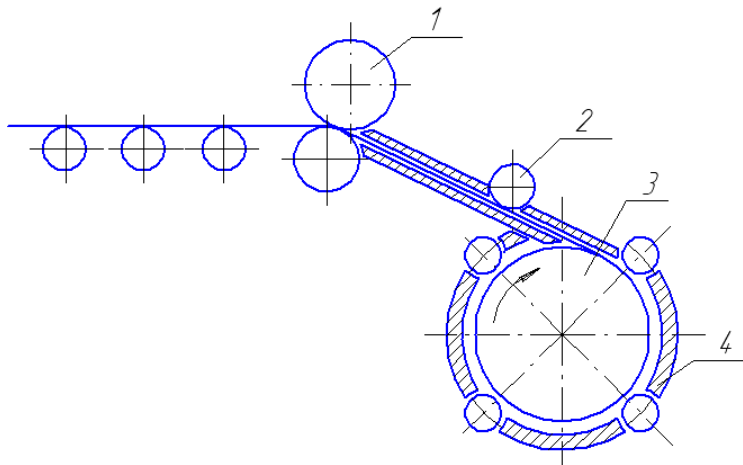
Схема роликовой барабанной моталки для горячей полосы:
